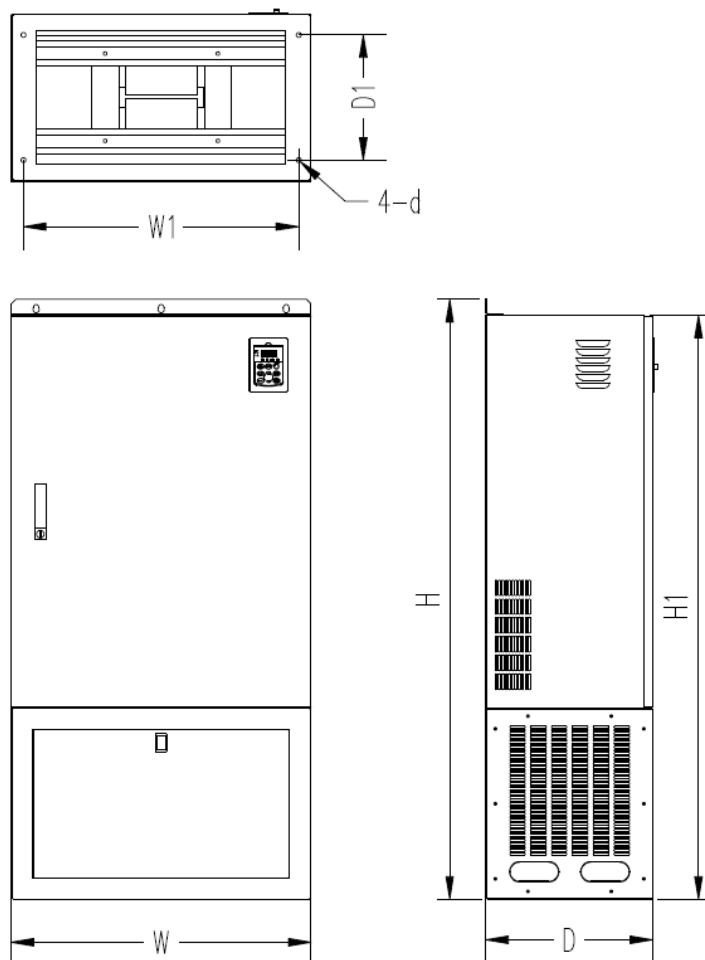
KOC700系列（带电位器）柜机结构外型尺寸及安装尺寸示意图
